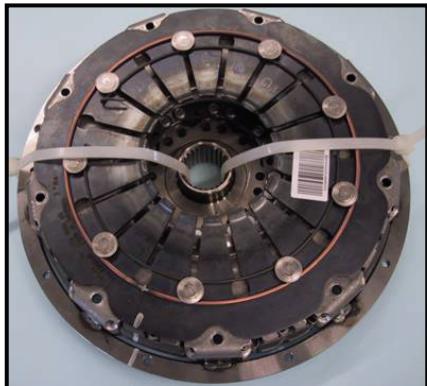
Vormontierter Zustand / Pre-assembled/ état assemblé / Embra-
